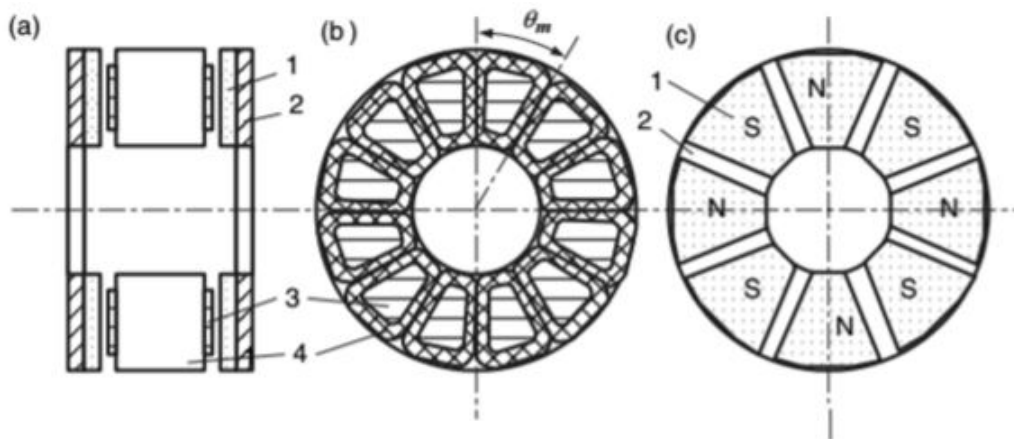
Machine à aimants permanents et flux axial à stator interne et double rotor externe (a) vue d'ensemble, (b) stator, (c) rotor, 1- aimants permanents, 2- disque du rotor, 3- pôles du stator, 4- Bobinages [22]
